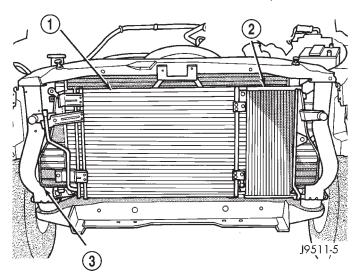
Condensador y enfriador auxiliar de la transmisión
